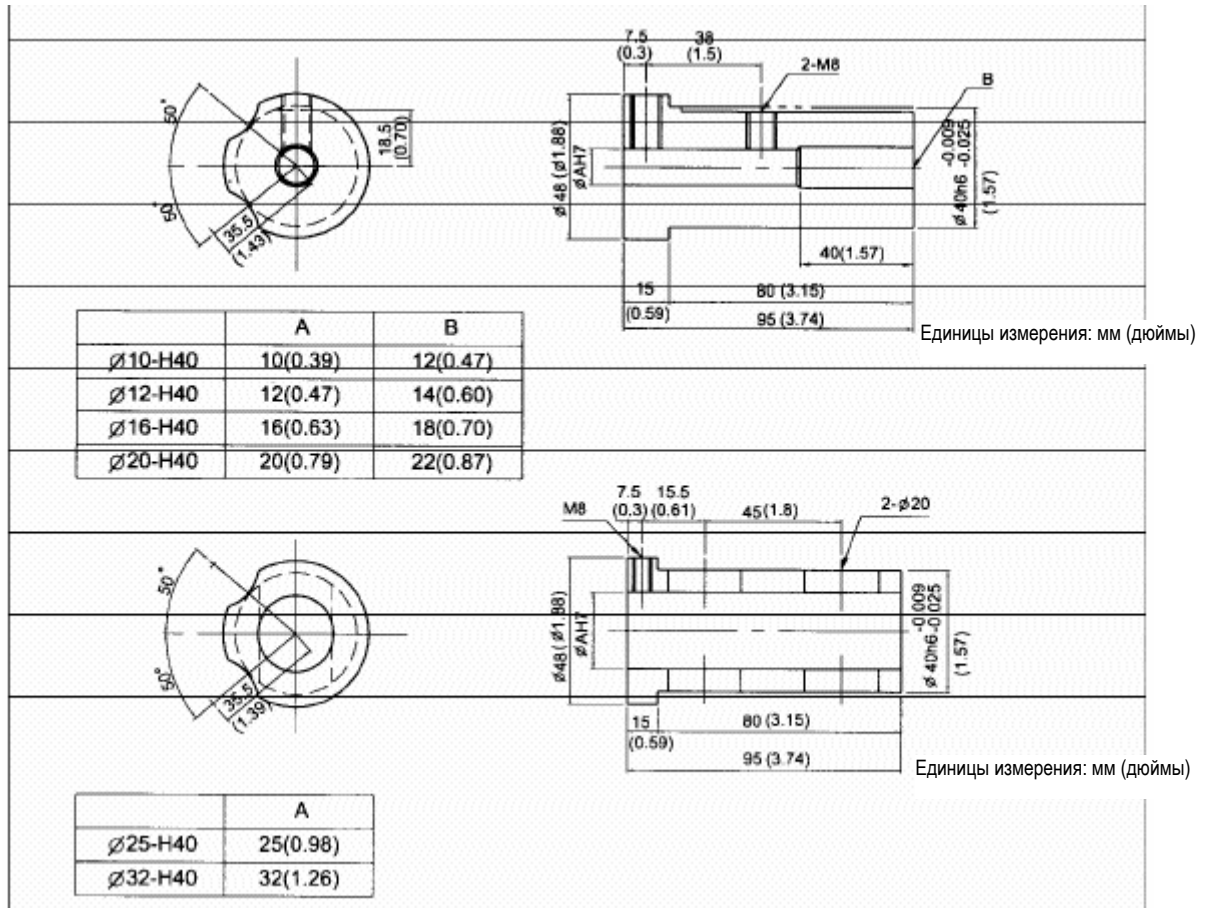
Габариты резцедержателя (втулка расточной оправки)
